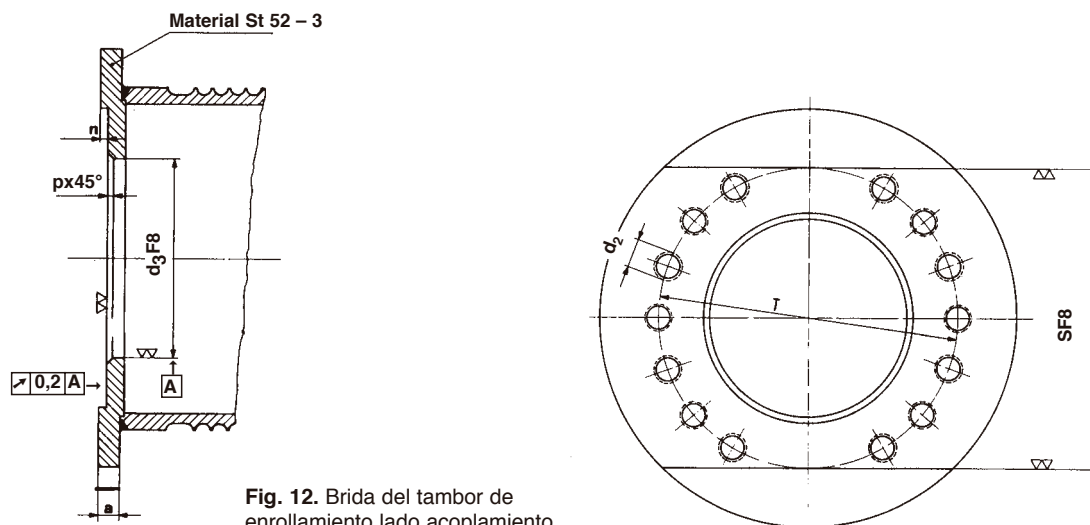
Brida del tambor de enrollamiento lado acoplamiento
